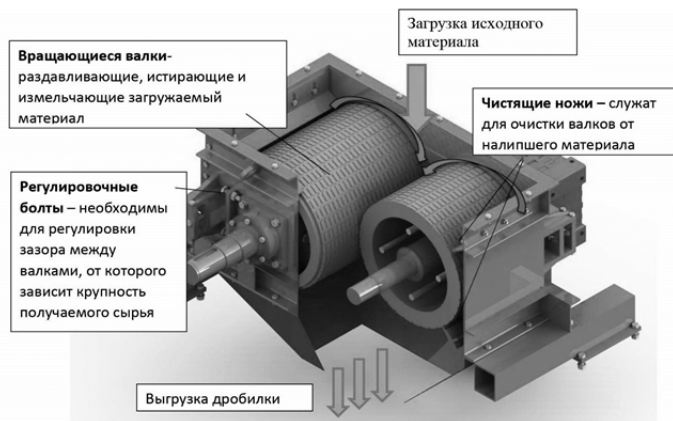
Типовая конструкция рабочего органа пресса валкового
